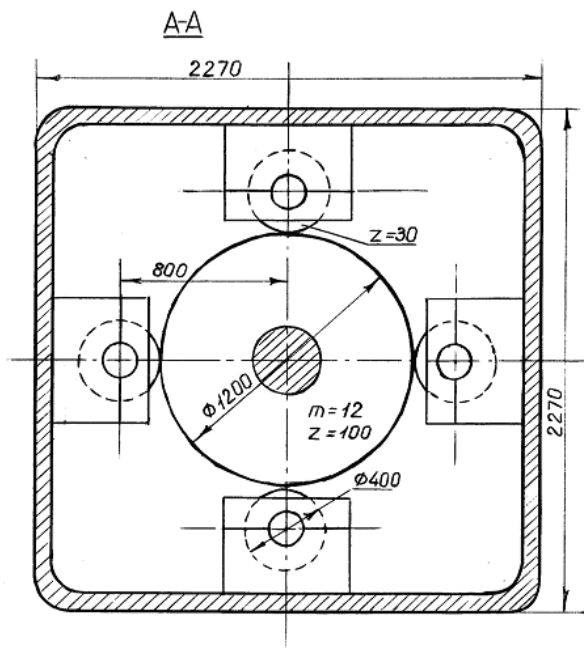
Привод вертикально клетки прокатного стана. Редуктор
